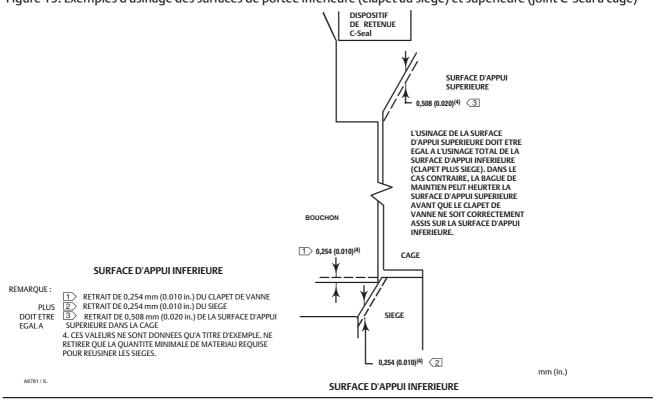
Exemples d'usinage des surfaces de portée inférieure (clapet au siège) et supérieure (joint C-Seal à cage)
